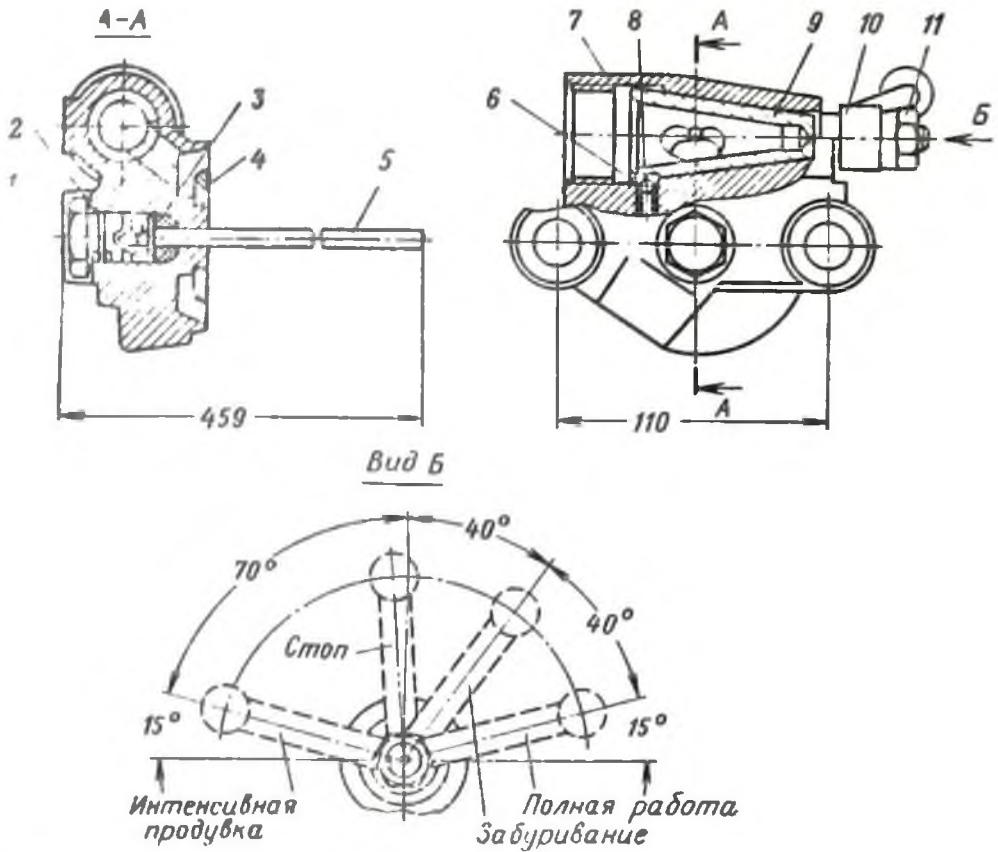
Корпус крана перфоратора ПР-25МВ:
